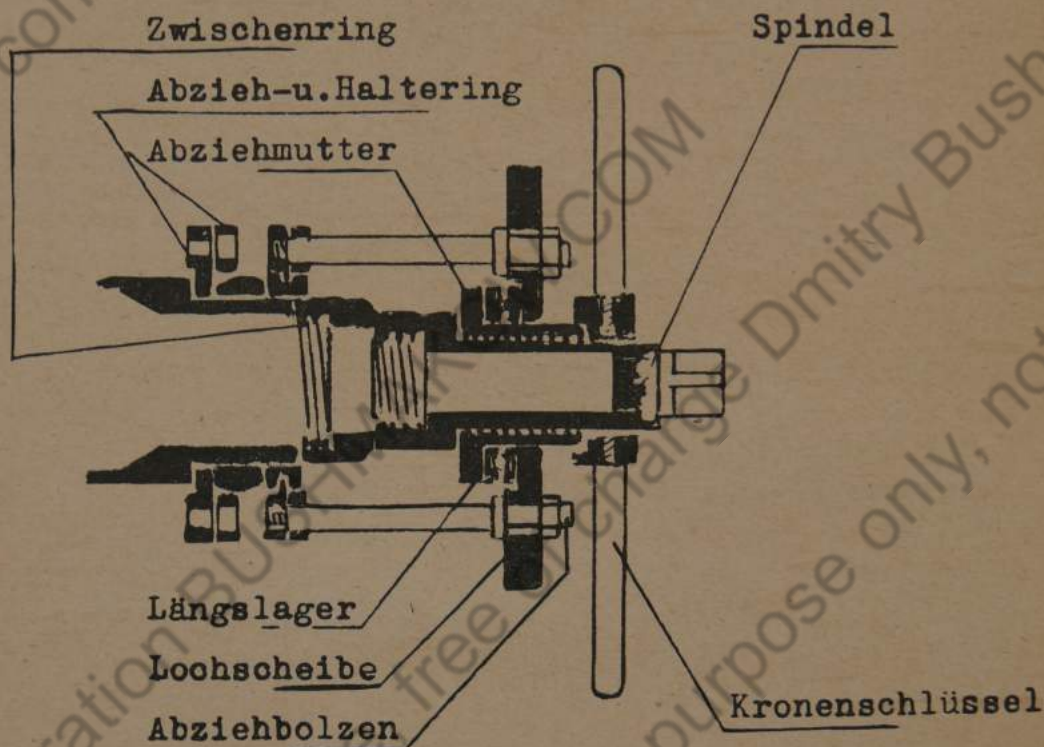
Abziehen des Halterings und des Rollenlagerinnenringes
